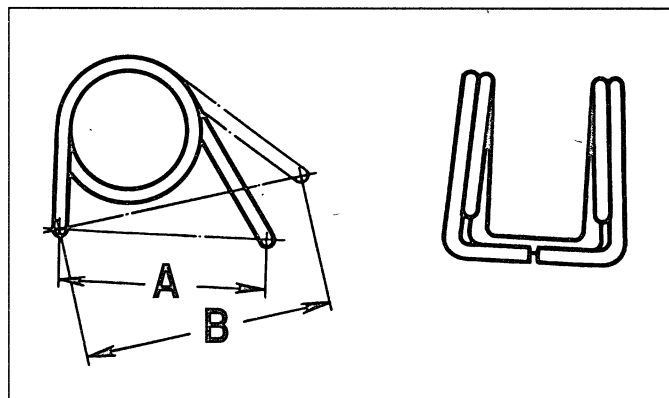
Схема проверки пружины рычага: А – размер в свободном состоянии; В – размер под нагрузкой
